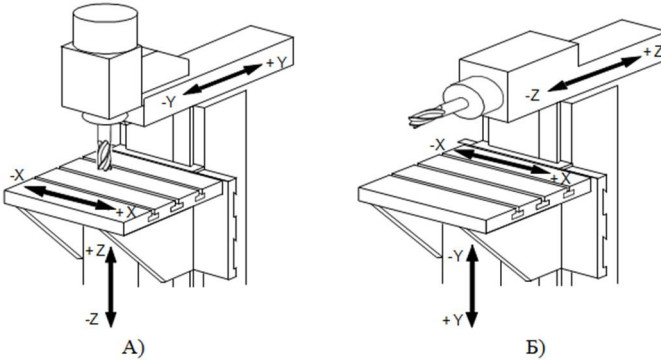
Система координат вертикально-фрезерного верстата (А) і горизонтально-фрезерного верстата (Б)
